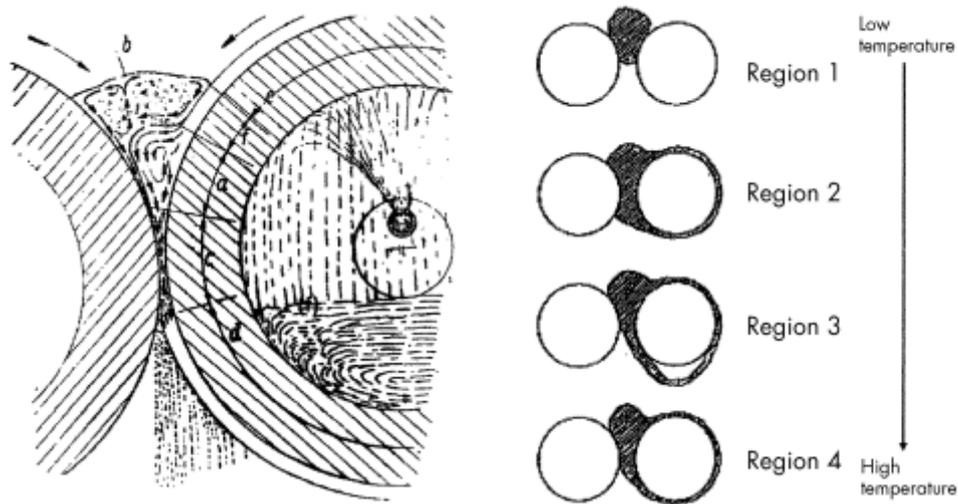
Lavorazione della gomma nella *Open rubber milling machine* (fonte: *Mill Behaviour of Rubber on Two Roll Mill with Temperature- Hiroyuki Ohtsuka<sup>1</sup> and Michiharu Toh*)
